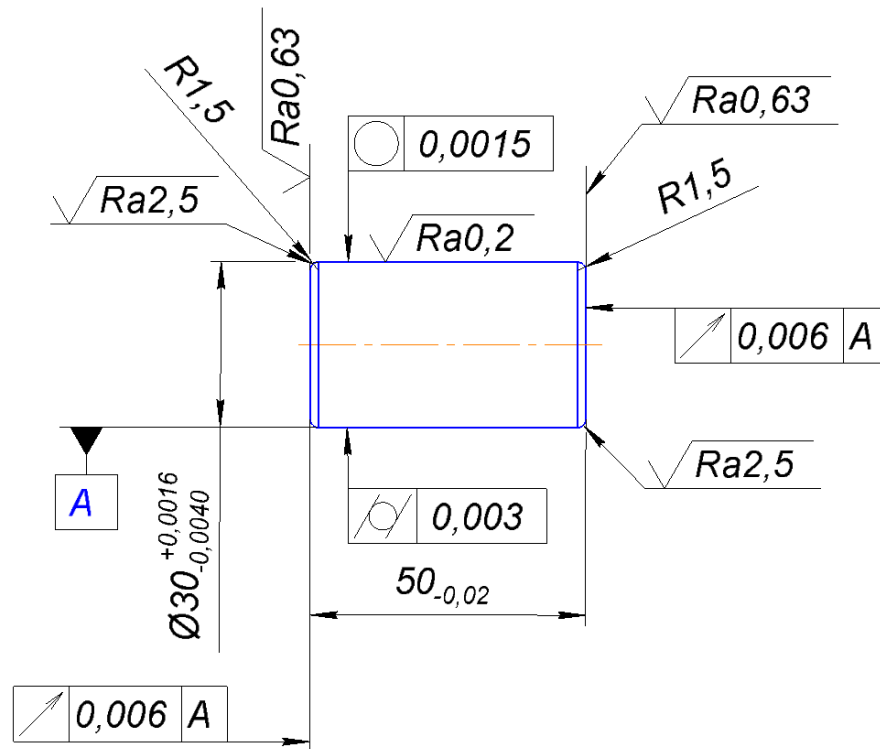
Креслення деталі «Ролик підшипника»
